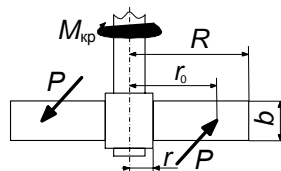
Схема нагрузок на двухлопастную мешалку
